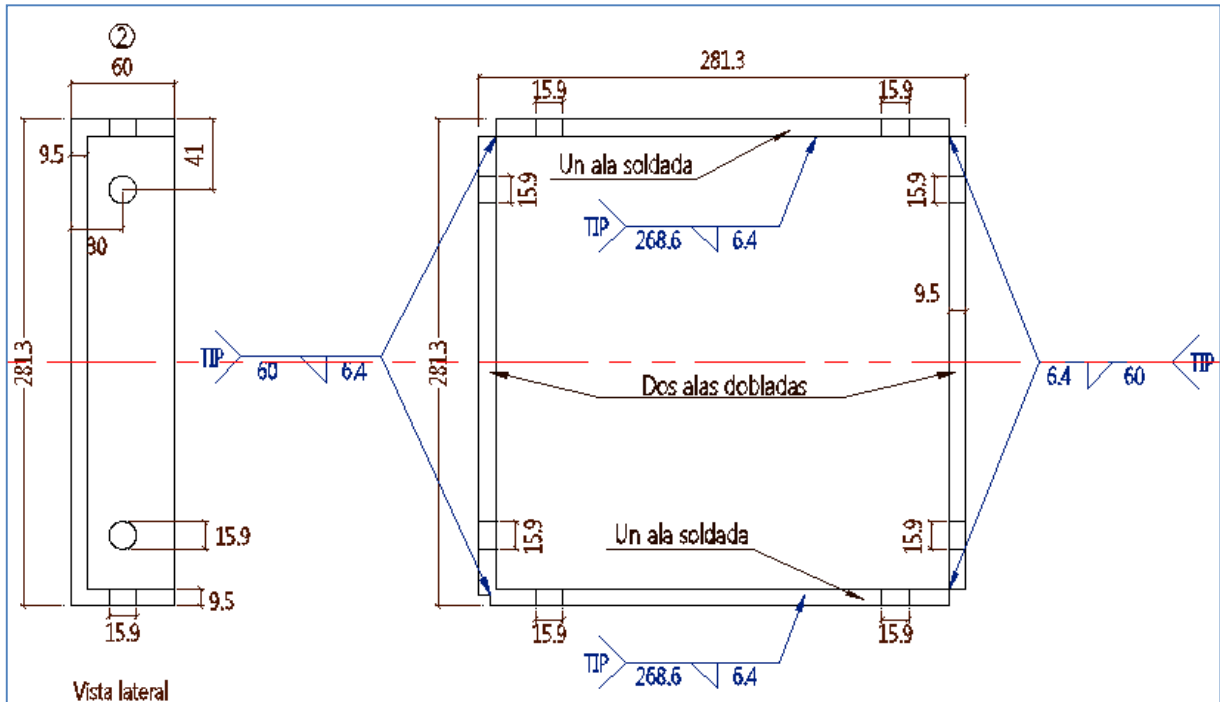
Detalle despiece pieza No.2 modelo 1 flexión.
